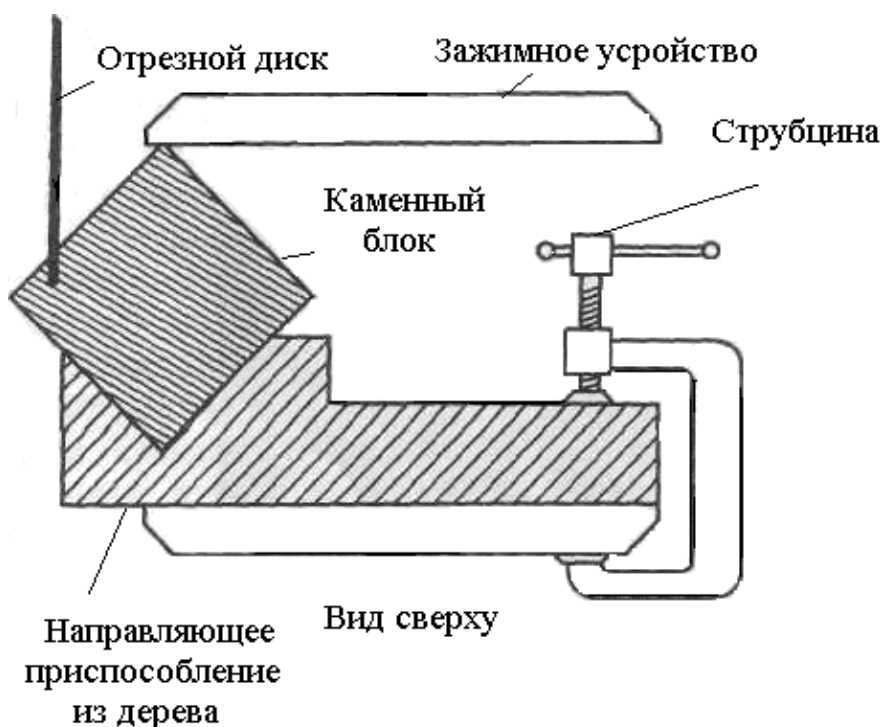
Деревянный кондуктор для опилования заготовок шаров
